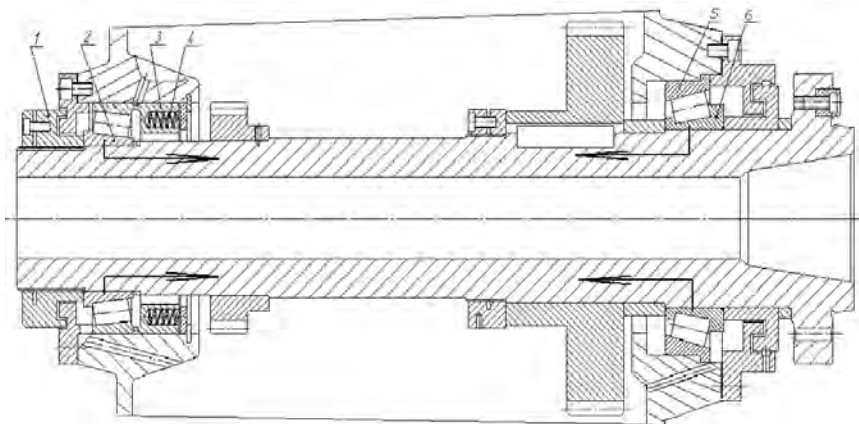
Шпиндельный узел с роликовыми радиально-упорными коническими однорядными подшипниками, установленными в опорах *встряжку
